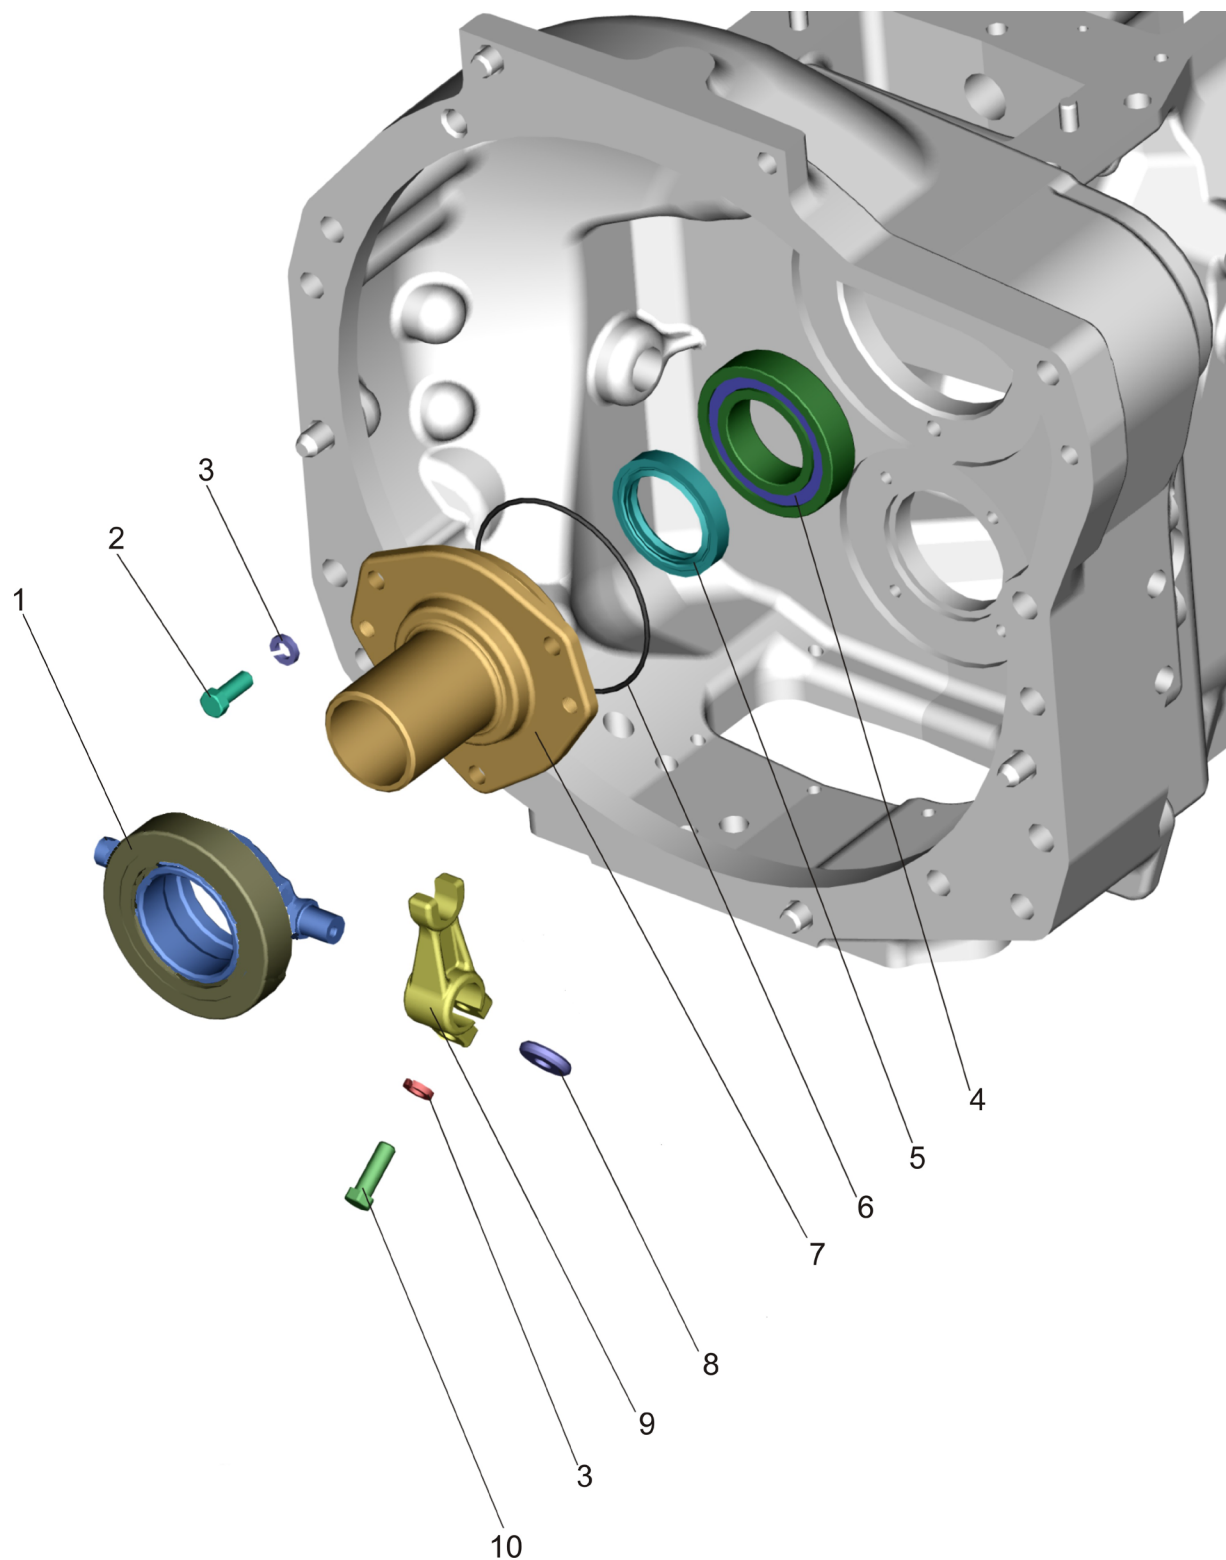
Корпус сцепления. Отводка (с установкой муфты LuK)
